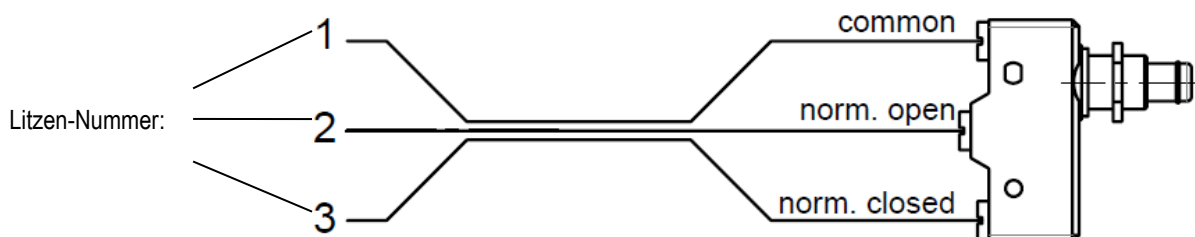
PVC-Steuerleitung für Endlagenschalter (flanschseitig)
